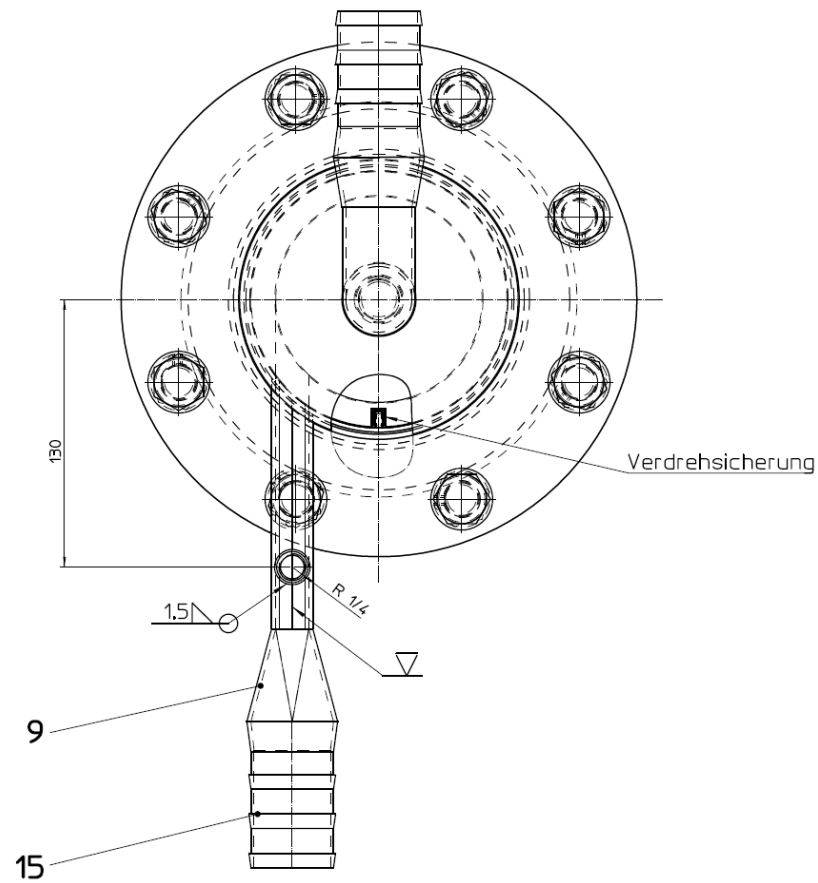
/4: Hydrozyklon Grundriss
